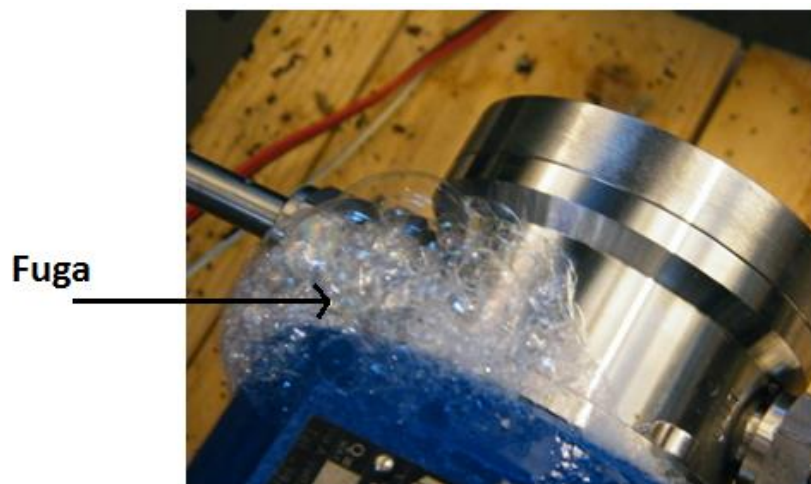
Água com sabão a reagir à fuga de gás na flange da bomba.
